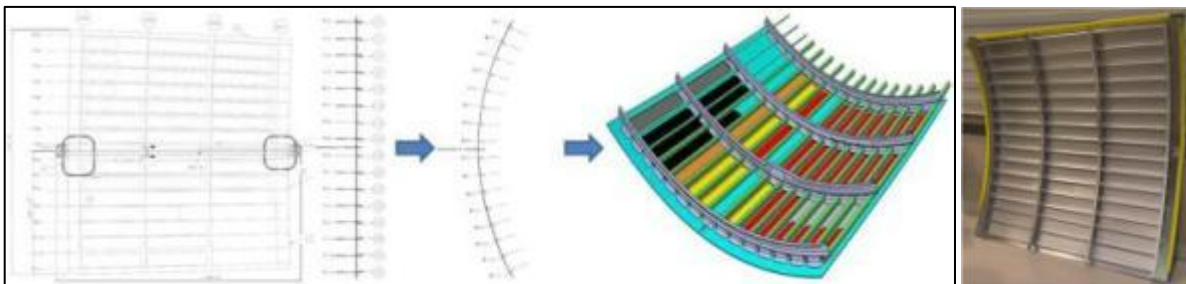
AlMgSc Blech mit FSW Naht, LBW geschweißte Stringer und Integralspanten
